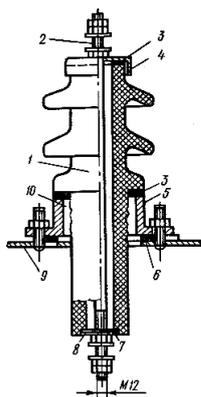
Армированный ввод 6-10 кВ наружной установки:
